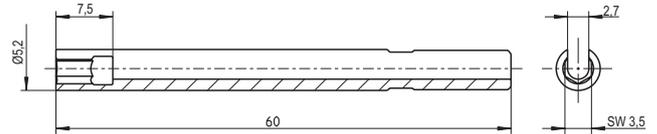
Montageschlüssel für Kabel Typ 1300A125
